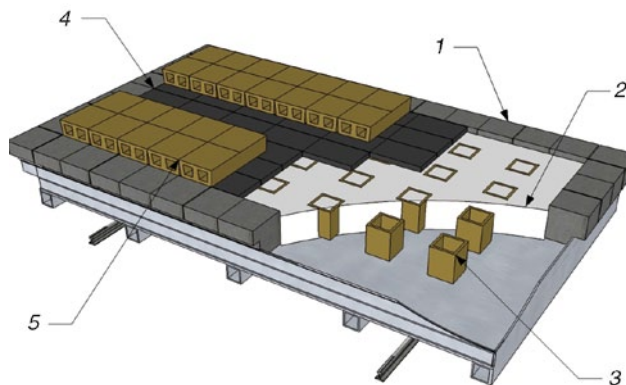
Конструкция футеровки вагонетки с использованием окантовочных блоков из жаростойкого бетона и канализованного пода из огнеупорной керамики: 1 – окантовочный блок из жаростойкого бетона; 2 – легкий теплоизоляционный вермикулитобетон или вермикулитовая засыпка; 3 – поддерживающий стакан огнеупорной керамики; 4 – подовые плиты из жаростойкого бетона; 5 – канализованный под из огнеупорной керамики
